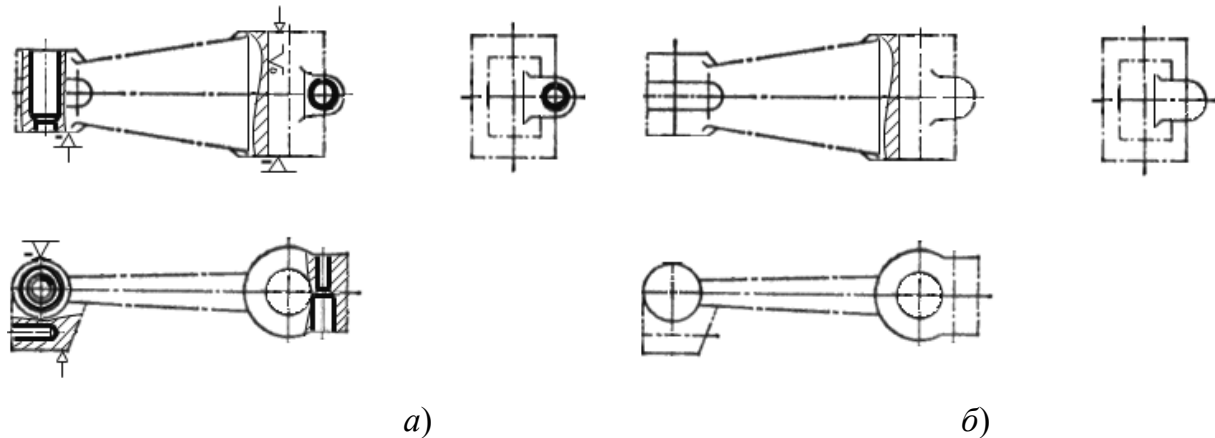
Эскизы: а – операционный эскиз со схемой установки; б – эскиз поступающей заготовки
